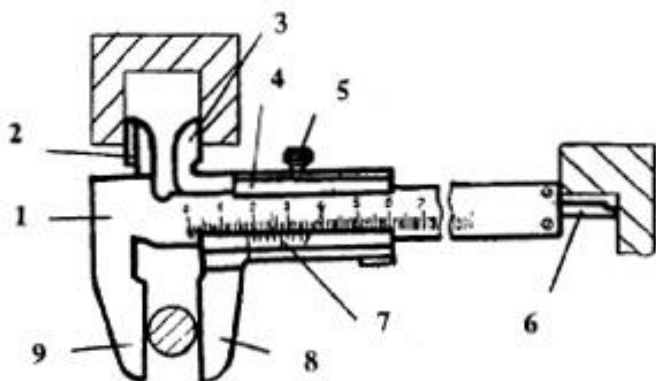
Штангенциркуль ШЦ-1: 1 — штанга; 2 — верхняя неподвижная губка; 3 — верхняя подвижная губка; 4 — подвижная рамка; 5 — зажимной винт рамки; 6 — глубиномер; 7 — нониус; 8 — нижняя подвижная губка; 9 — нижняя неподвижная губка
